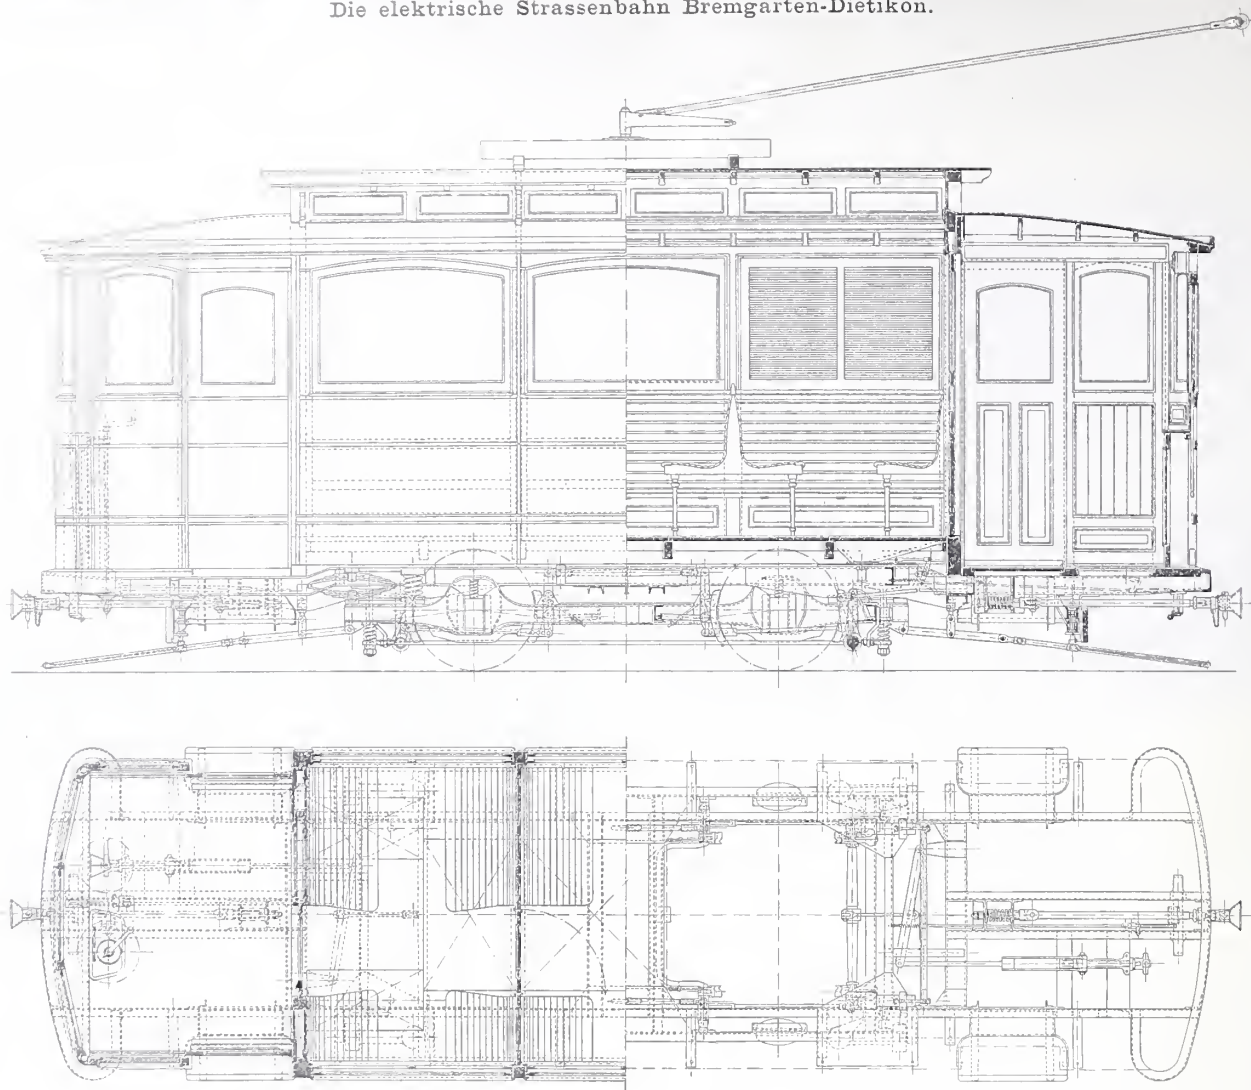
Motorwagen. — Ansicht, Grundriss und Schnitte. — Masstab 1:50.
